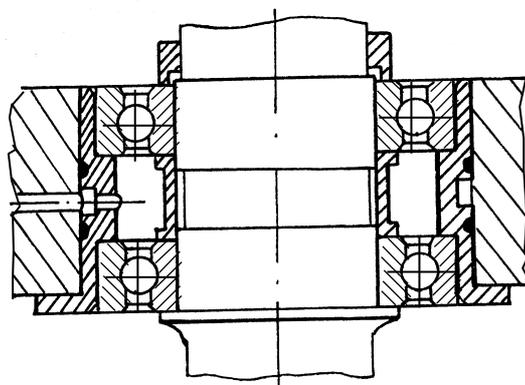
Способ уплотнения резиновыми кольцами гильзы подшипников
